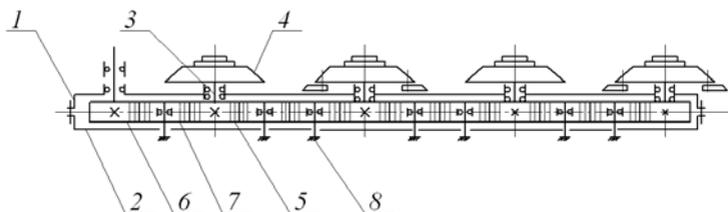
Схема привода роторов от зубчатой цилиндрической передачи
